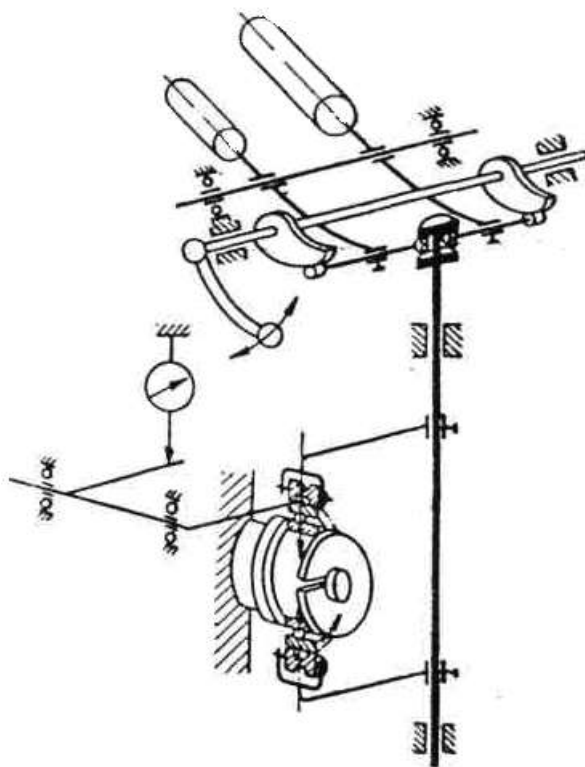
Схема измерений радиального зазора подшипника прибором Р123
